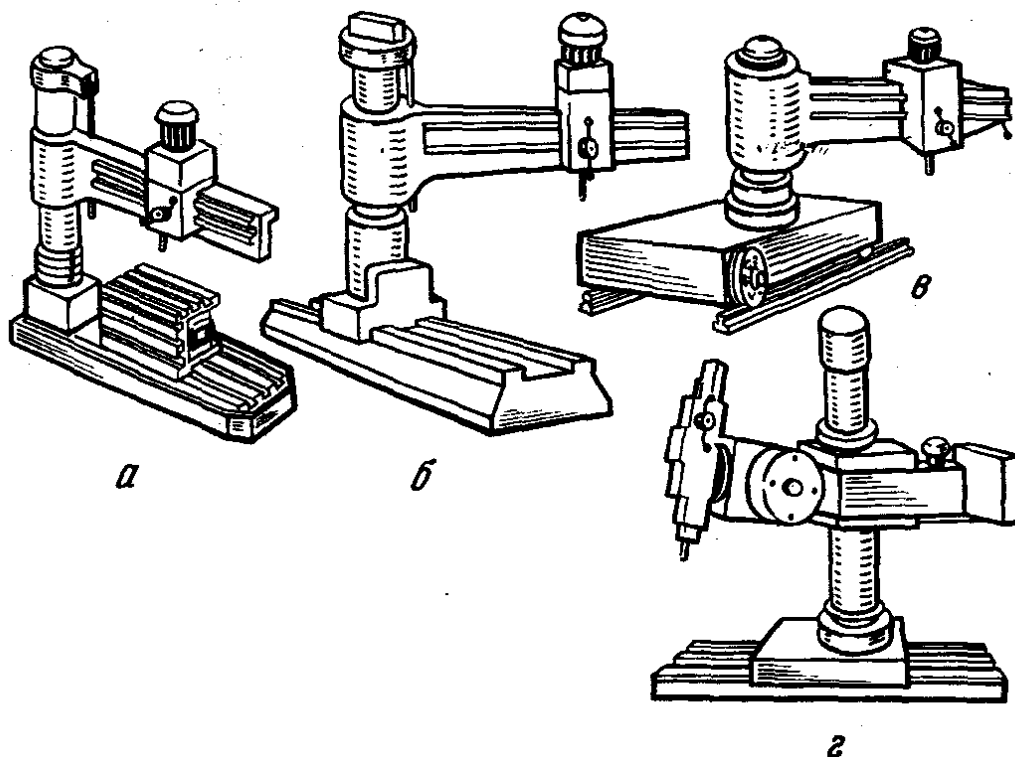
Компоновка радиально-сверлильного станка.
